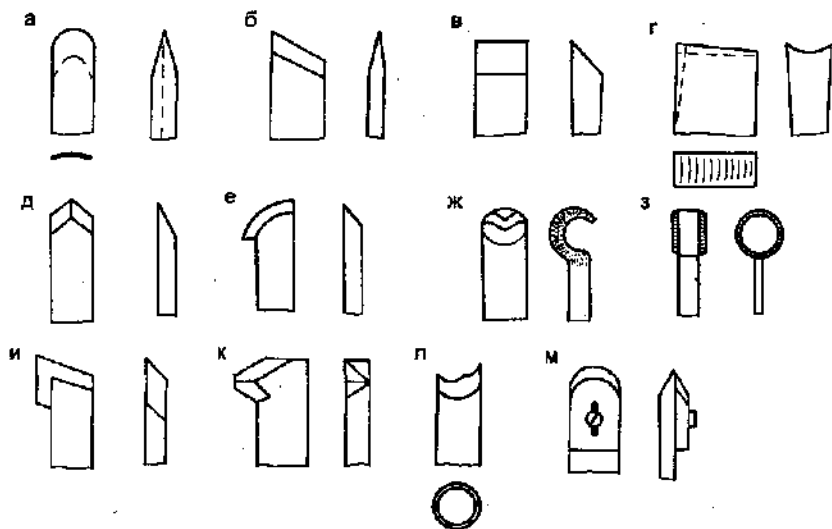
Резцы для ручного точения древесины: а — полукруглый; б — плоский косой; в — отрезной; г — отрезной с фигурной заточкой; д — угловой; е — фасонный; ж — ложечный резец-крючок; з — ложечный резец-кольцо; и — скошенный угловой; к, л, м — специальные
